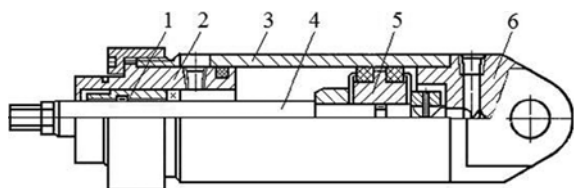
Чертеж гидроцилиндра типа ПЦ
